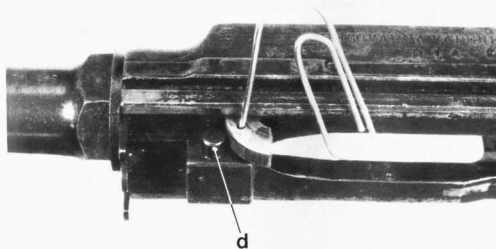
Zur Demontage des Beschleunigerhebels kann der Führungstift mit einem dünnen Draht zurückgedrückt werden. d = Anschlagstift.
